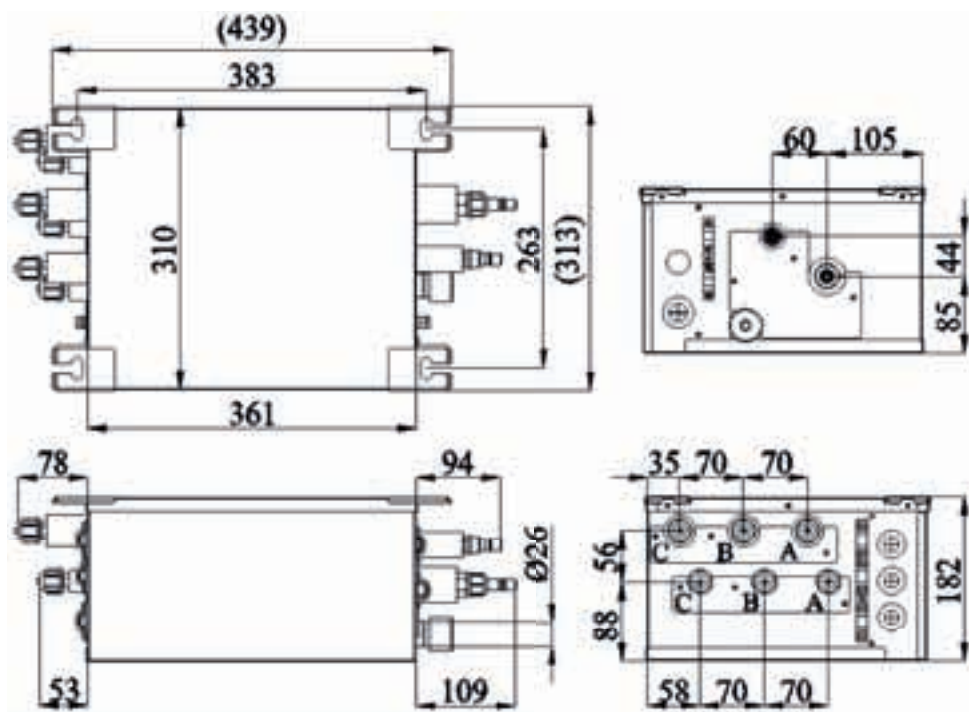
Габаритные и установочные размеры блока FXA3C-K (ед. изм.: мм)
